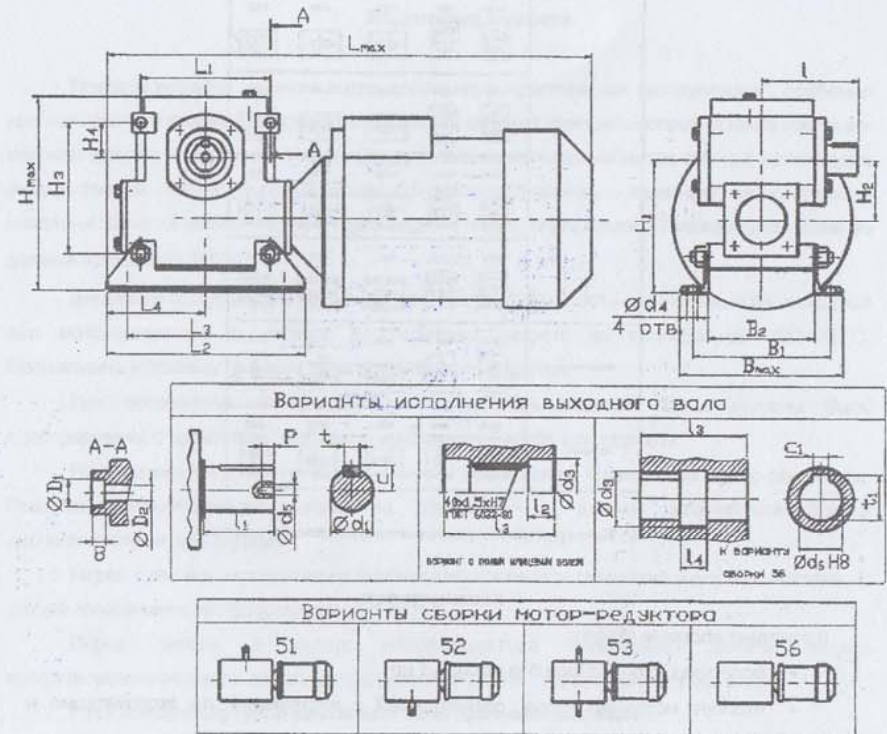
Габаритные и присоединительные размеры, варианты сборки
